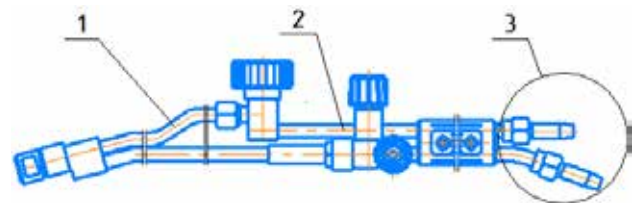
Газокислородный инжекторный резак РЗ-ФЛЦ
